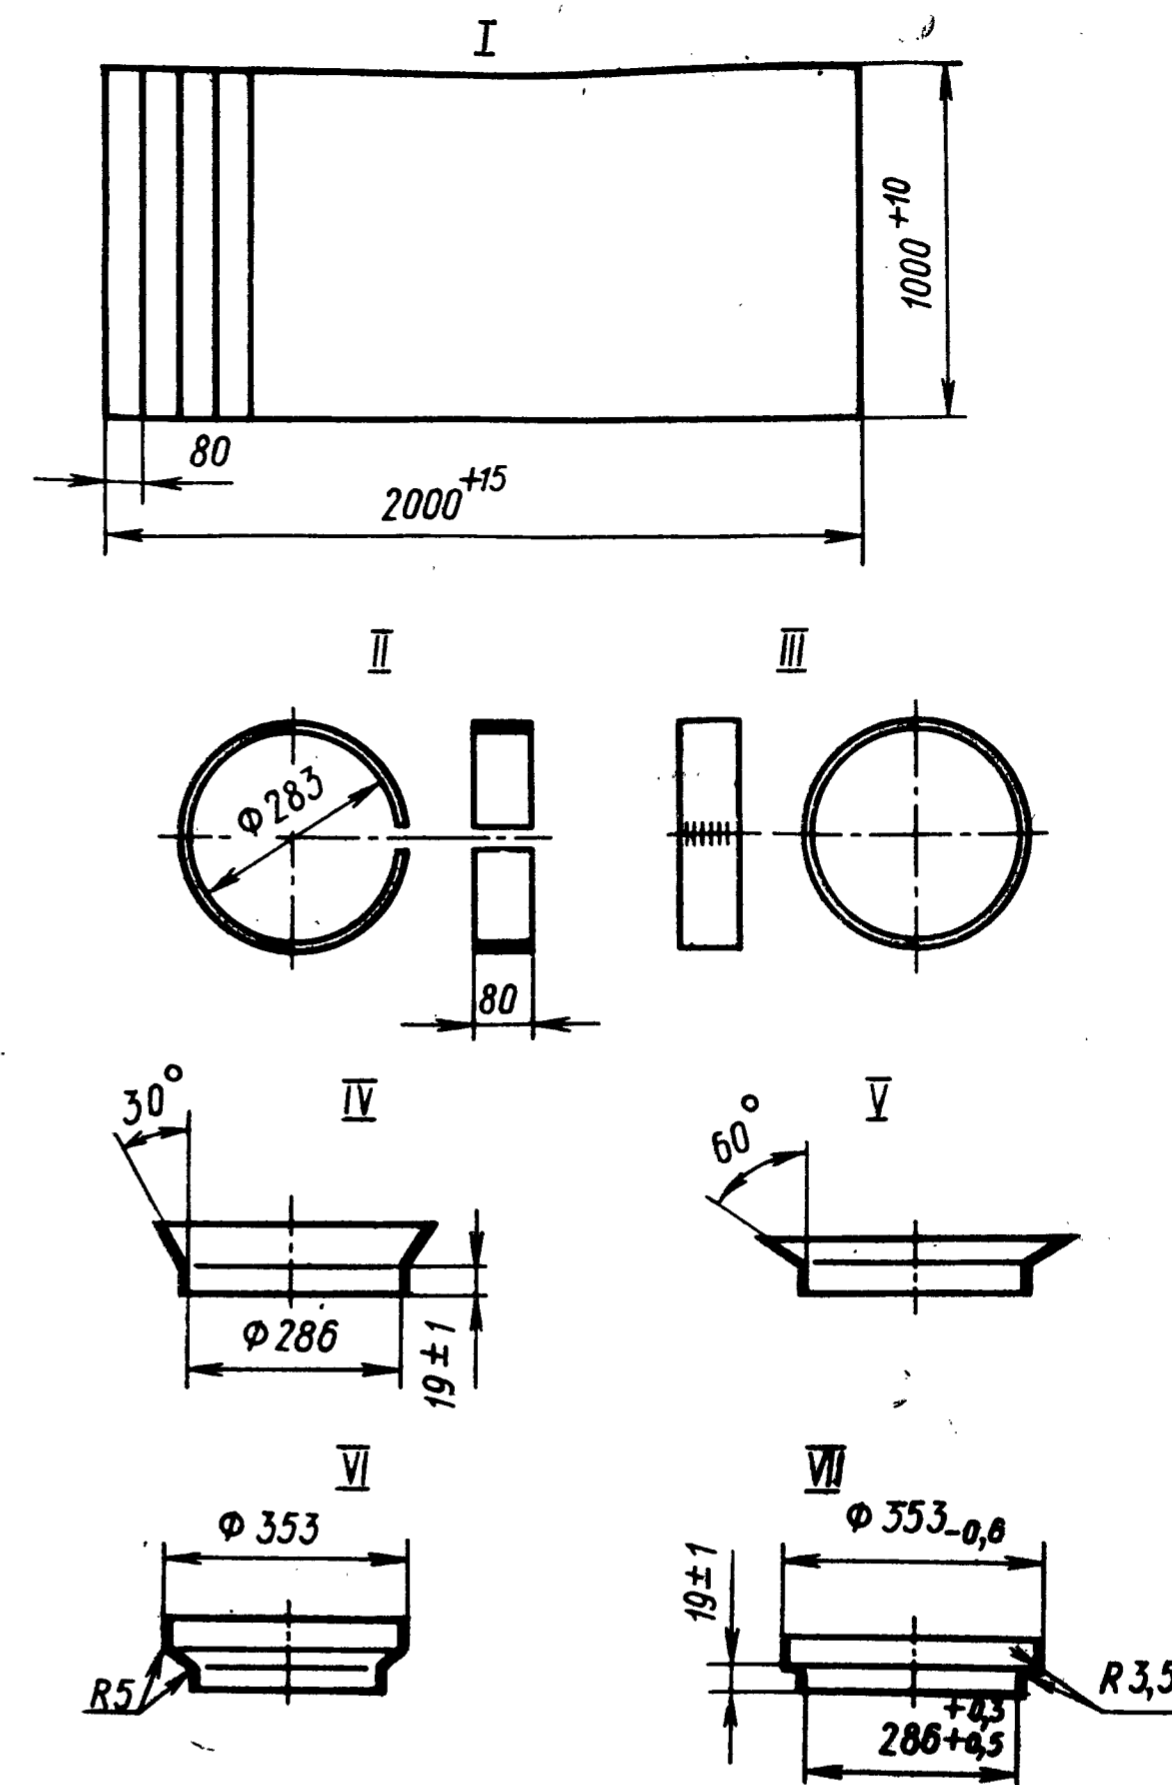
Технологический процесс изготовления ступенчатого кольца из сварной цилиндрической заготовки растяжением с развальцовкой и наружной отбортовкой
